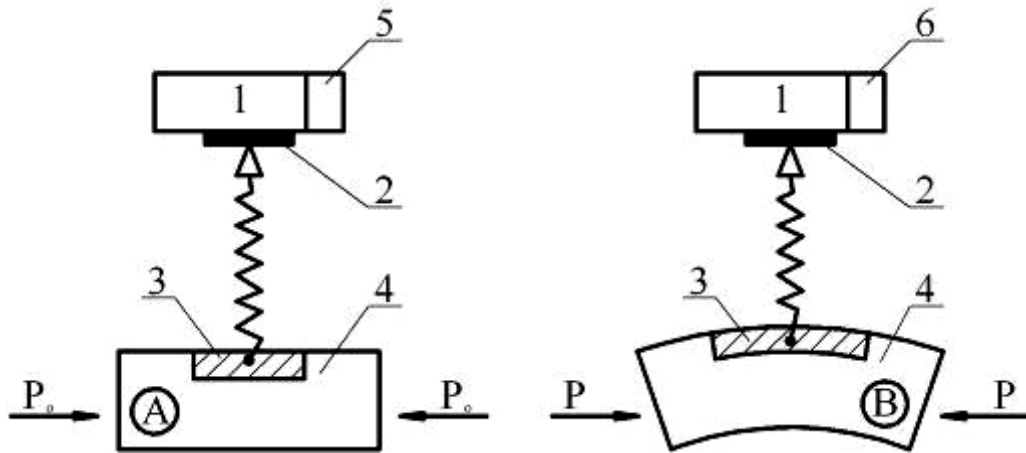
Схема неразрушающего контроля состояния изделия (образец, инструмент, деталь):
